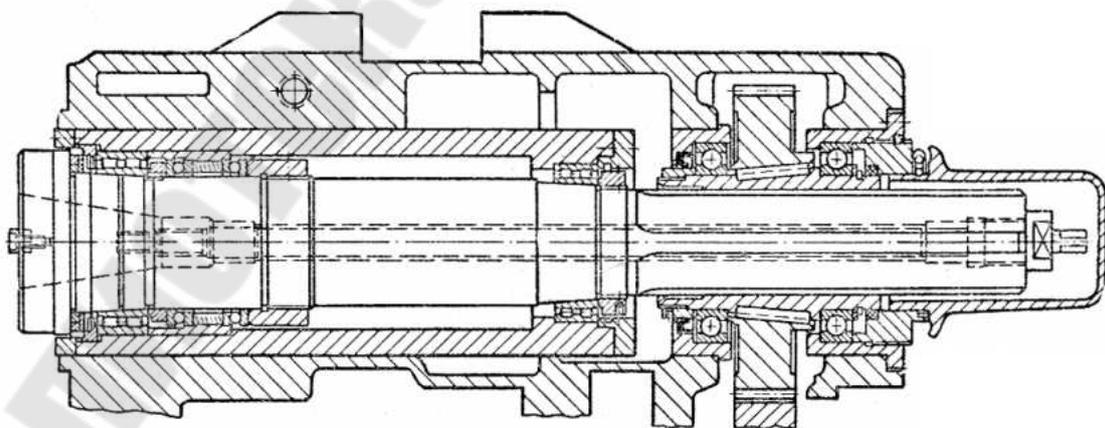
Шпиндельный узел фрезерного станка с упорными шарикоподшипниками
